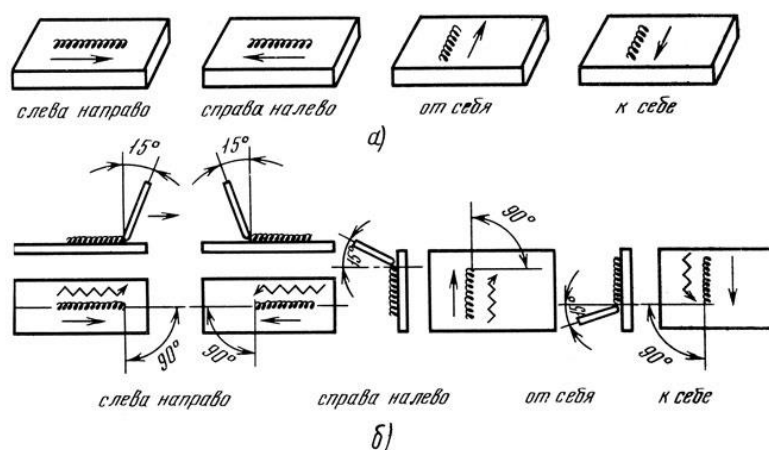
Направления сварки (а) и наклон электрода (б)
